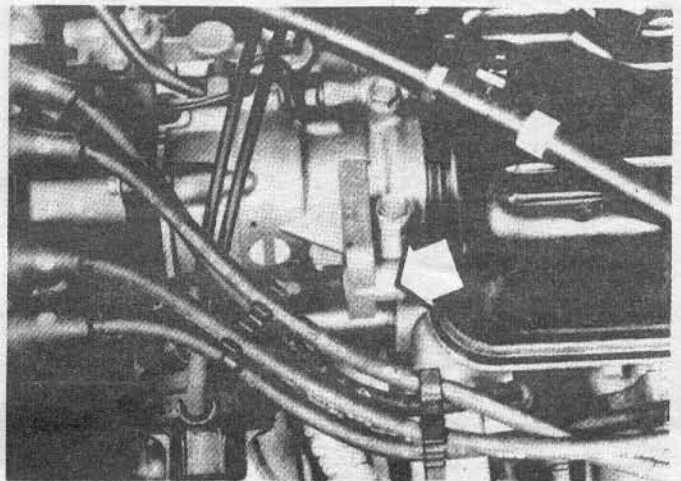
б ... и метки положения корпуса относительно головки цилиндра.
